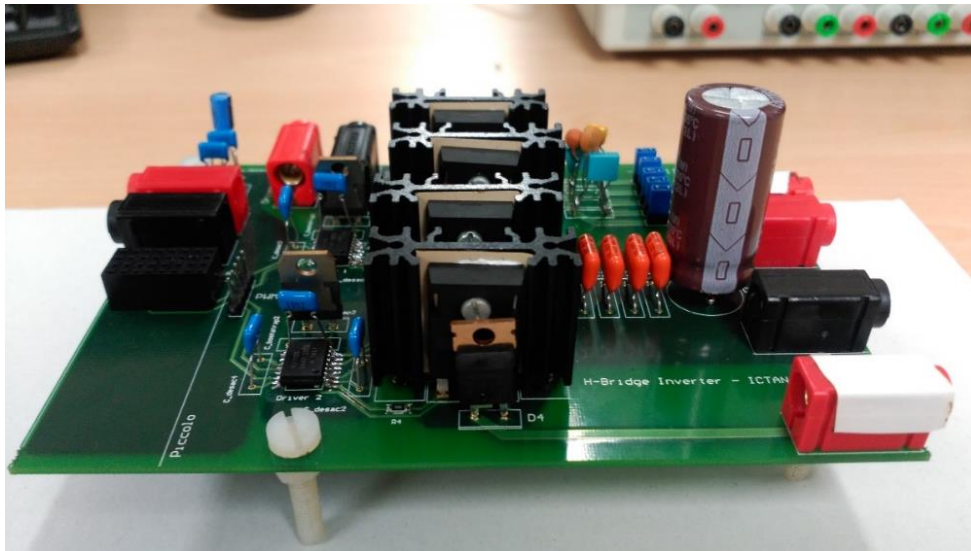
Vista frontal de la PCB después de soldadura y montaje de componentes
